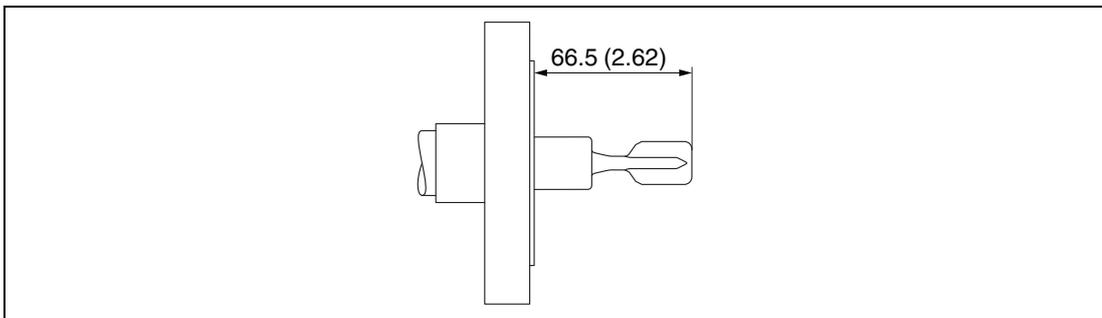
Beispiel mit Flansch, Maßeinheit mm (Zoll)
